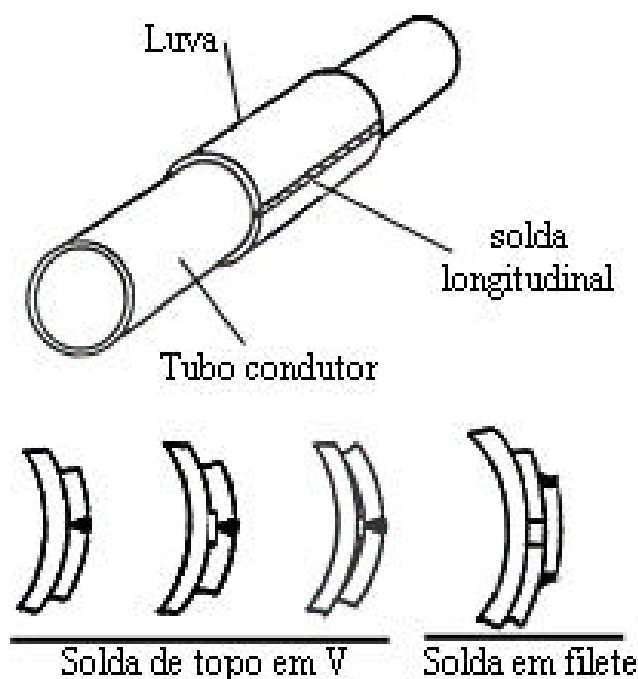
Soldagem de luvas tipo A. (Kiefner,1994)
